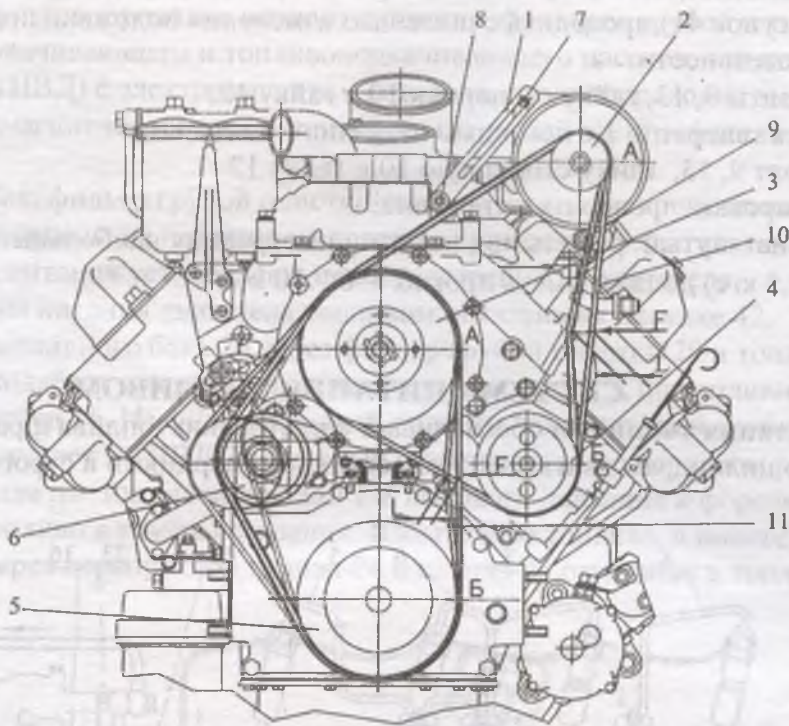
Схема проверки натяжения ремней для двигателей с гидромуфтой
